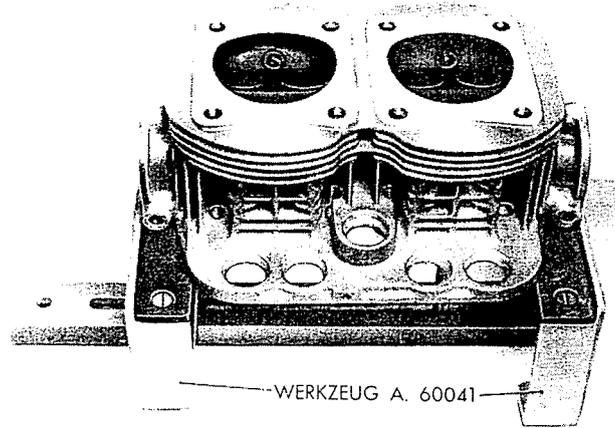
Werkzeug A. 60041 zur Ueberholung des Zylinderkopfes auf der Werkbank.
